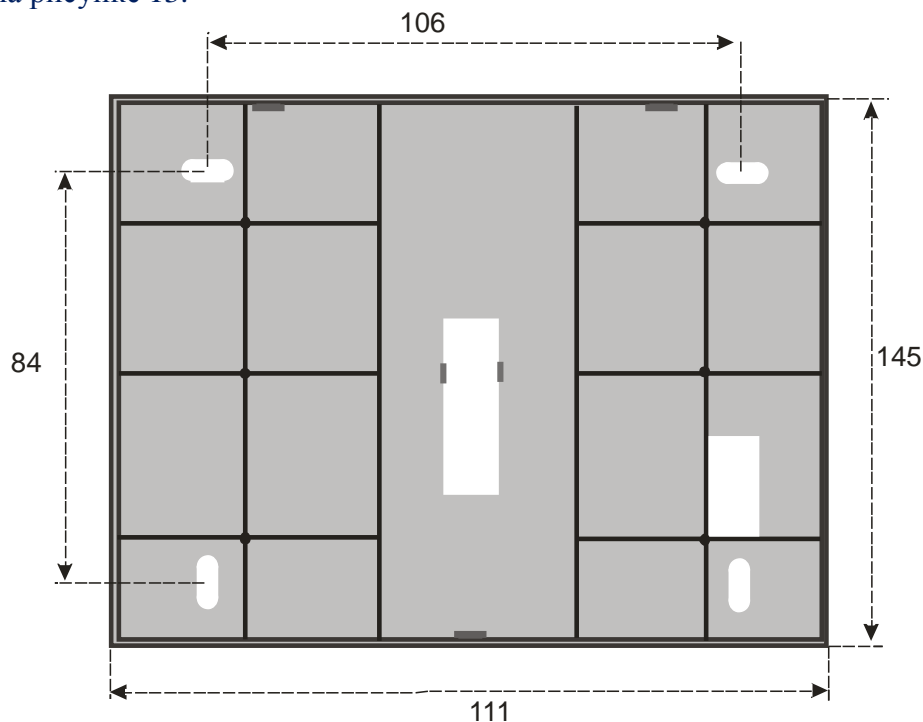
Внешний вид основания корпуса ВПУ и установочные размеры
